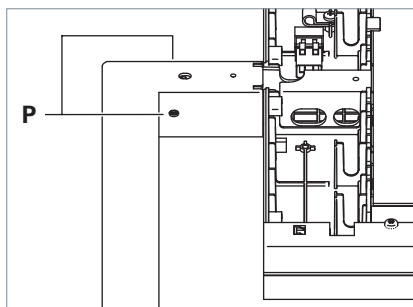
Allineamento della testa dell'apparecchio d'illuminazione ad angolo retto rispetto al tubo di supporto.
